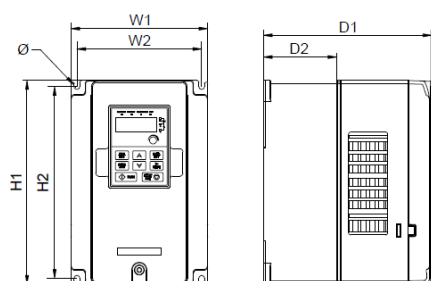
Настенный монтаж 4 – 37 кВт
